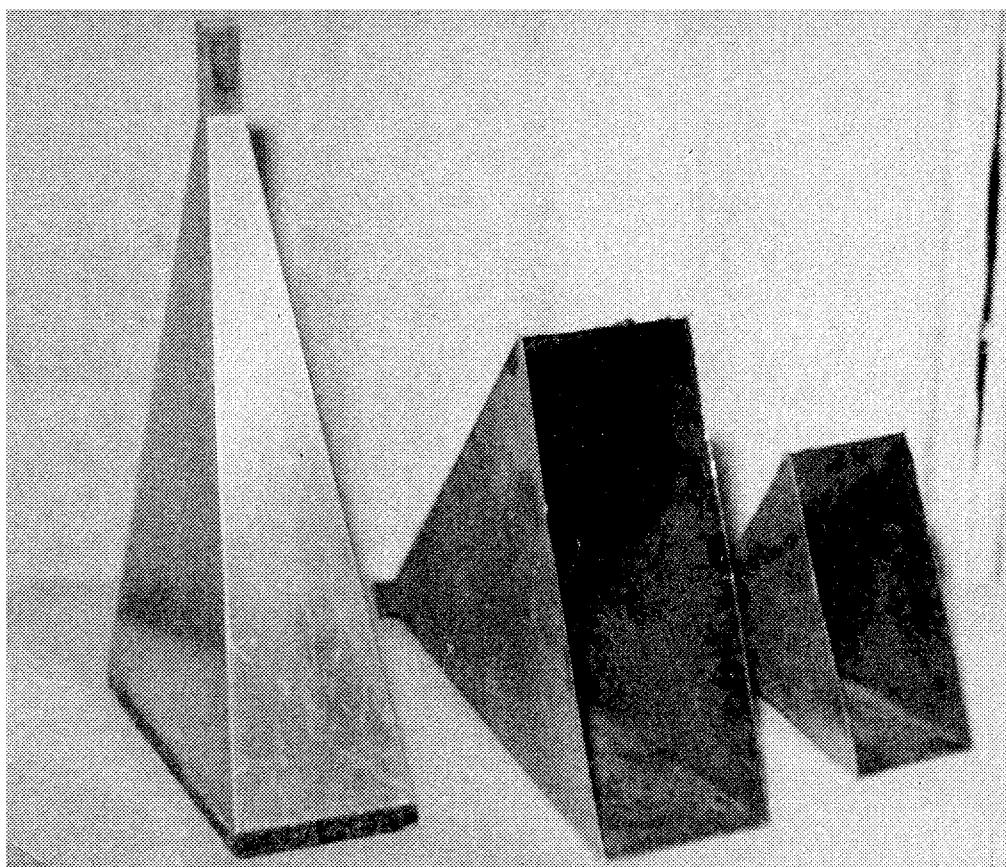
Матрица для изготовления и изготовленные рупорные антенны
